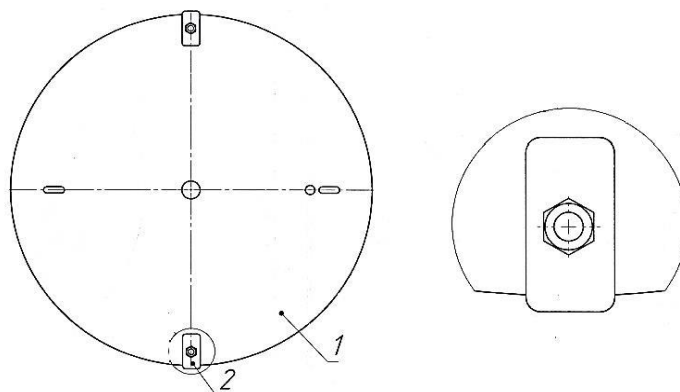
Нижняя стальная крышка устройства УЗЛ-Т ССД с установленными заглушками. 1 – диск; 2 – задвижка с болтом и гайкой, вид сверху. Гайка запорного механизма на рисунке не показана.
